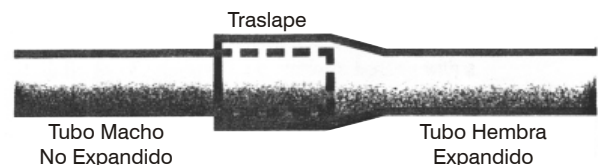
Tubo dentro de la Conexión Unión Soldada
